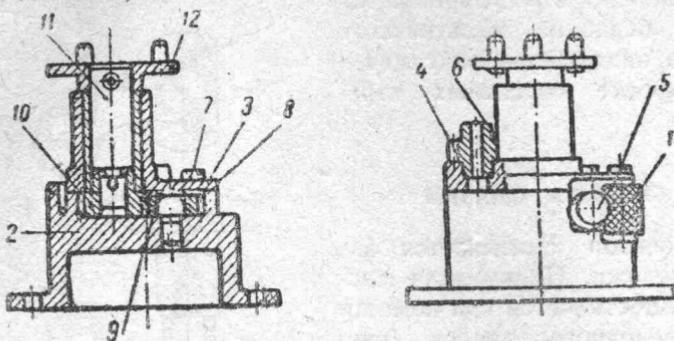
Насос в разрезе: 1 — сетка; 2 — корпус насоса; 3 — вал насоса; 4 — прокладка; 5 — винт; 6 — штуцер; 7 — винт; 8 — штифт; 9, 10 — шестерни; 11 — валик; 12 — фланец
